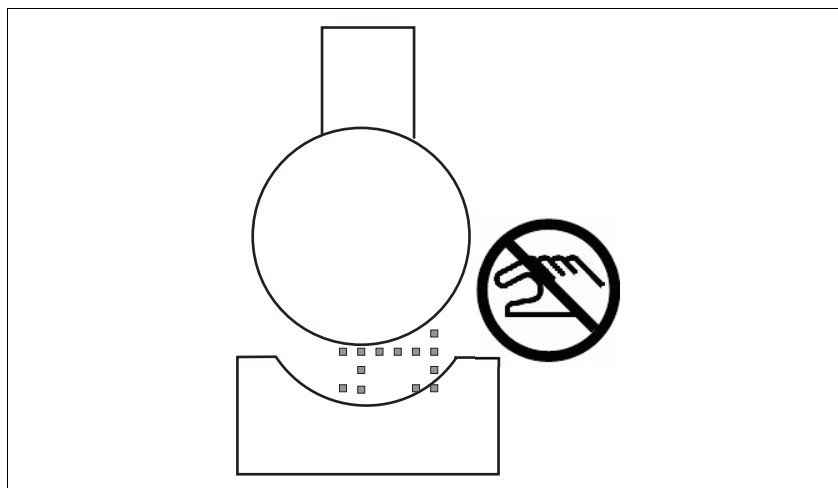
Quetschstellen bei Werkzeug breiter als das Schutzfeld
